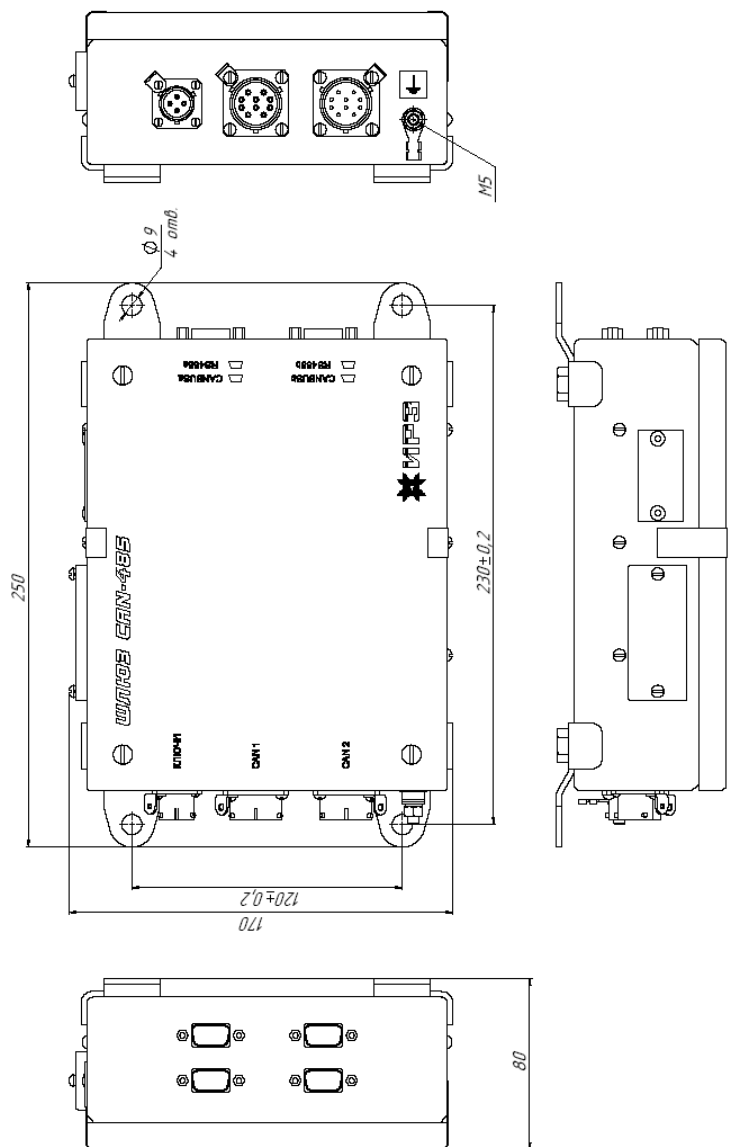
Внешний вид, габаритные и установочные размеры изделия
